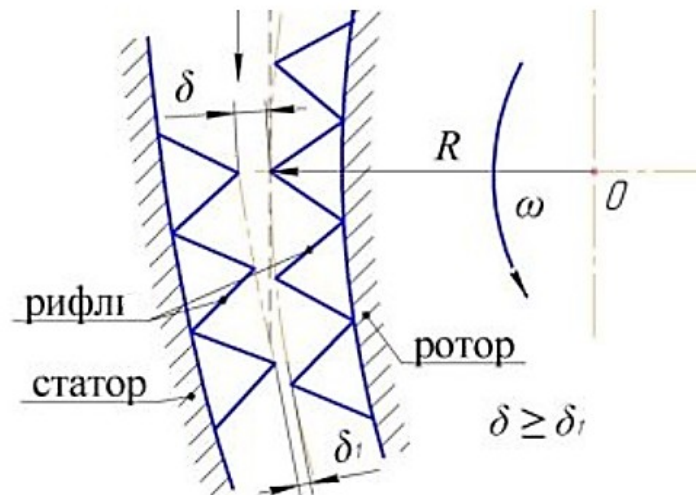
Схема робочих поверхонь статора і ротора
